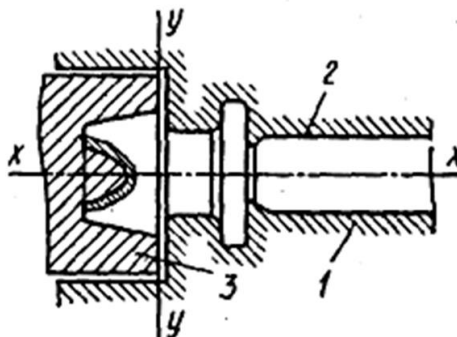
Схема штамповки на ГКМ: 1 – неподвижная часть матрицы; 2 – подвижная часть матрицы; 3 – пуансон
